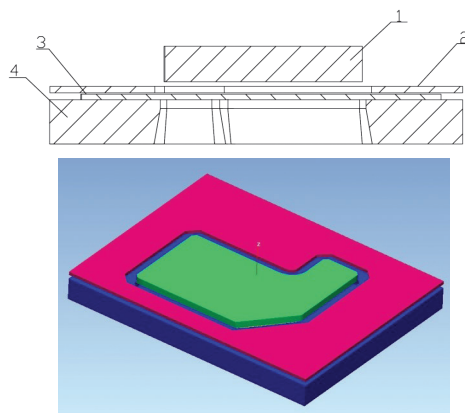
Модель вырубного штампа: 1 – пуансон; 2 – прижим; 3 – заготовка; 4 – матрица
